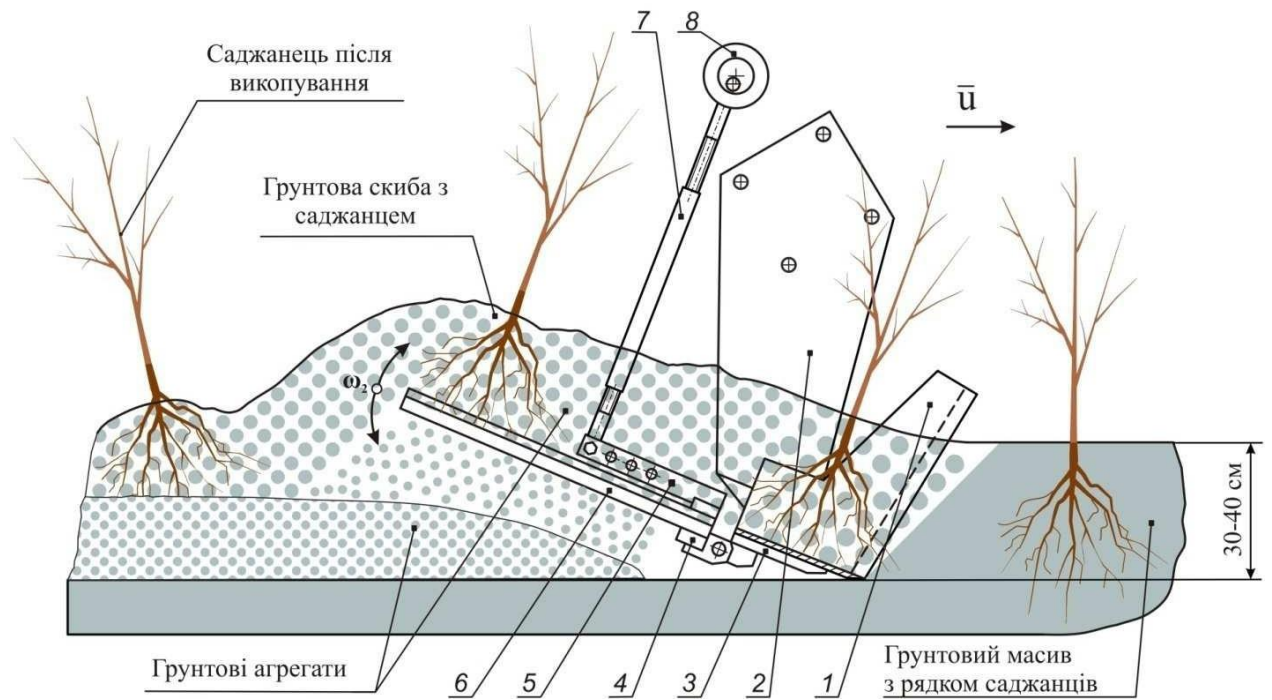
Конструктивно-технологічна схема робочого органу викопувального плуга для викопування саджанців: 1 – робоча скоба для викопування; 2 – опорна стійка; 3 – башмак; 4 – траверса; 5 – важільний механізм; 6 – розпушувач ґрунту; 7 – ексцентрикова тяга; 8 – ексцентриковий механізм.
